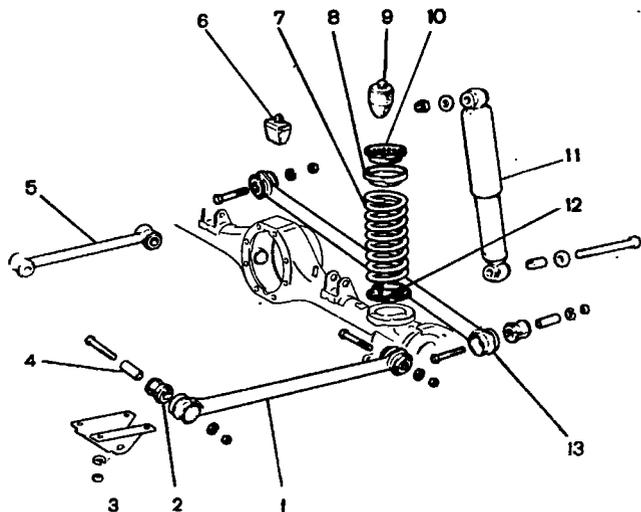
Детали задней подвески: 1 - нижняя продольная штанга; 2 - резиновая втулка; 3 - кронштейн крепления нижней продольной штанги к кузову; 4 - распорная втулка; 5 - верхняя продольная штанга; 6 - дополнительный буфер хода сжатия; 7 - пружина; 8 - верхняя чашка пружины; 9 - буфер хода сжатия подвески; 10 - верхняя изолирующая прокладка пружины; 11 - амортизатор; 12 - нижняя изолирующая прокладка пружины; 13 - поперечная штанга
